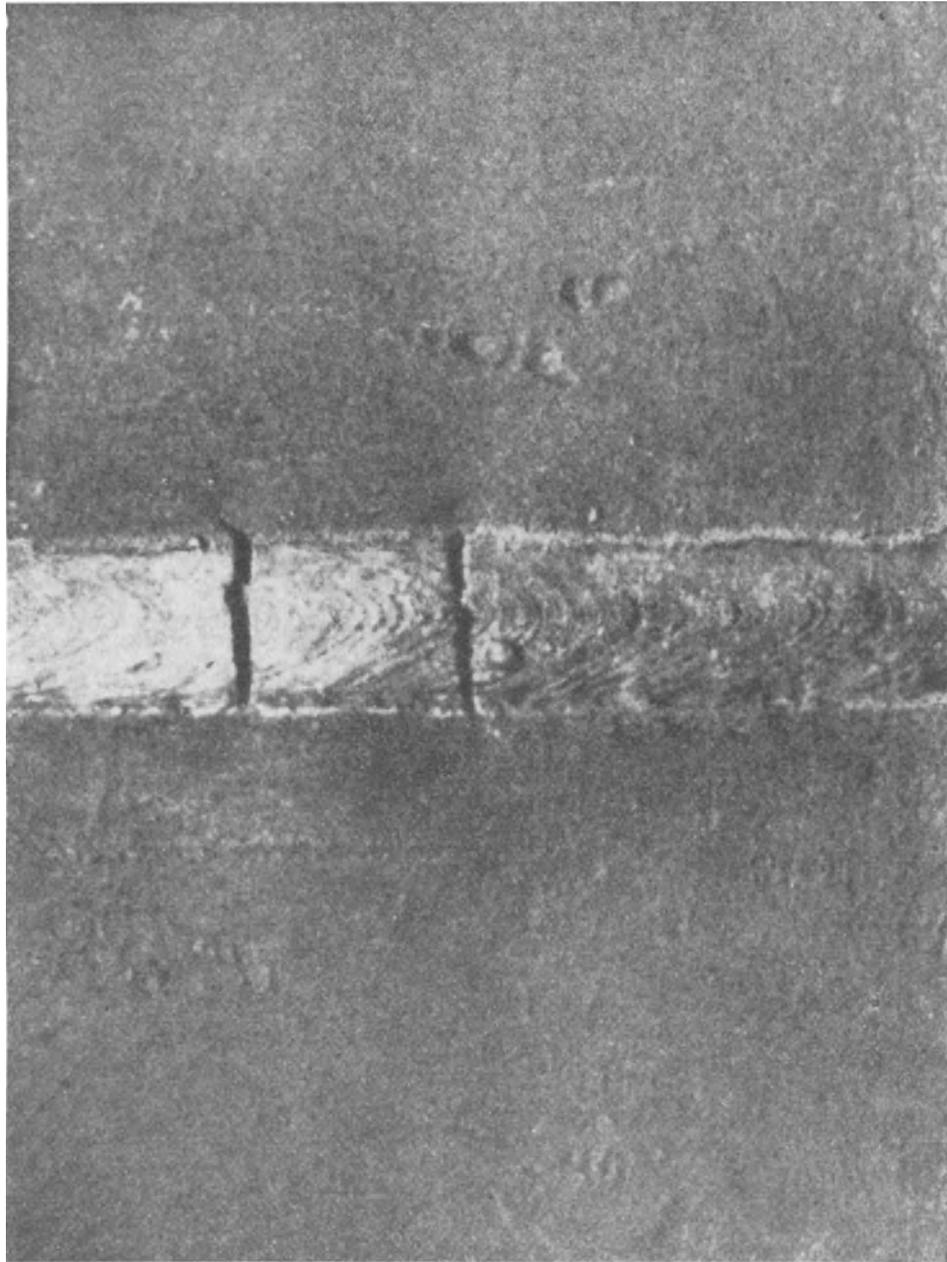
Querrisse in längsbeanspruchter Schweißnaht.
